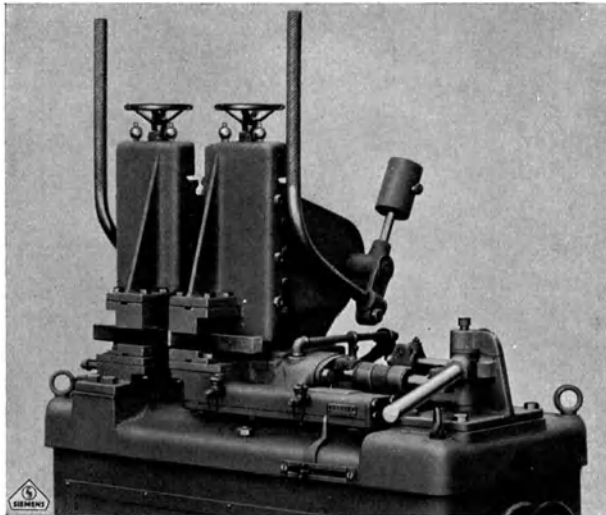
Stumpfschweißmaschine mit Schnellspannung und Kniehebelstauchung (Hersteller: Siemens-Schuckert-Werke).
